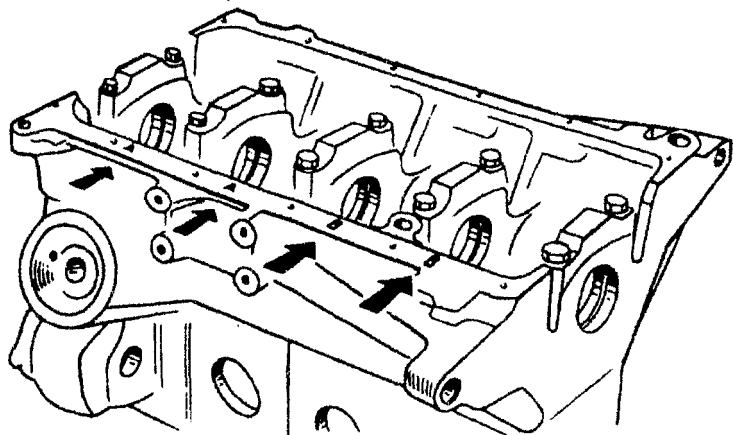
Буквенная маркировка размерного класса цилиндров на блоке двигателя
